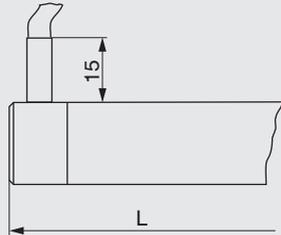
Wegsensor Typ - CR mit integriertem Kabel (radial)
